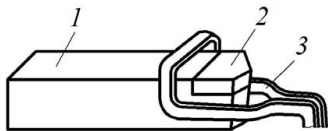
Установка индуктора для пайки режущей пластины однолезвийных инструментов:
